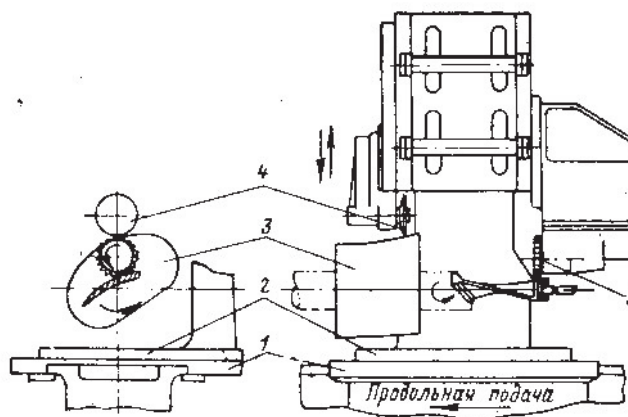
Схема кругового фрезерування пера лопатки вузькими поперечними строчками.
